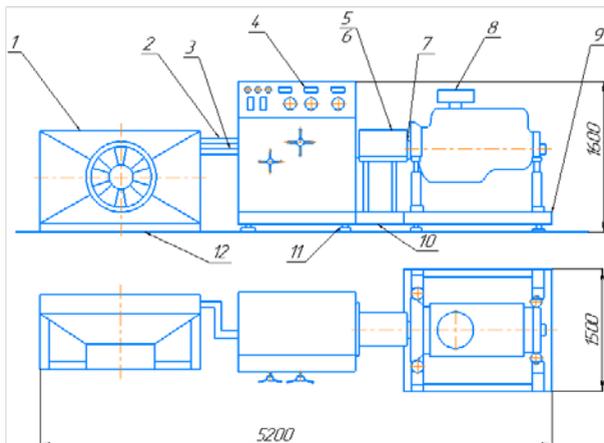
Общий вид разрабатываемого обкаточно-тормозного стенда с гидрообъемным приводом для обкатки ДВС:
